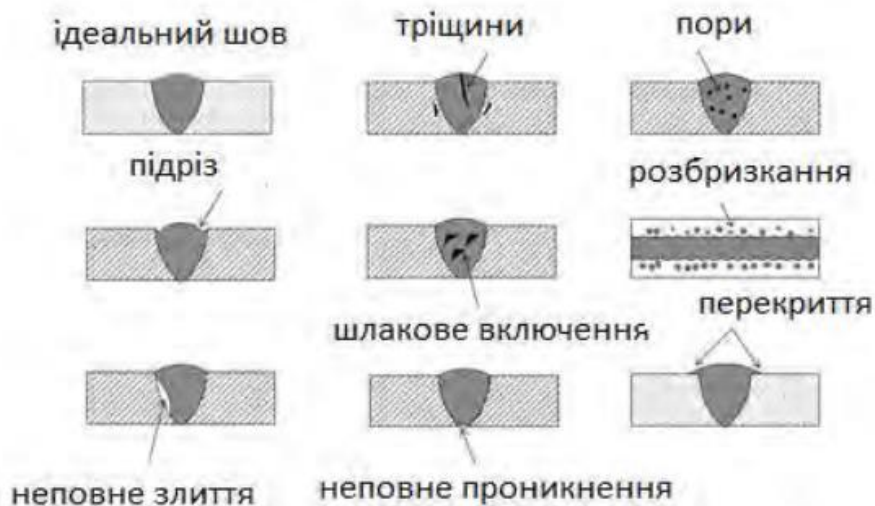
Різні види дефектів зварного шва
